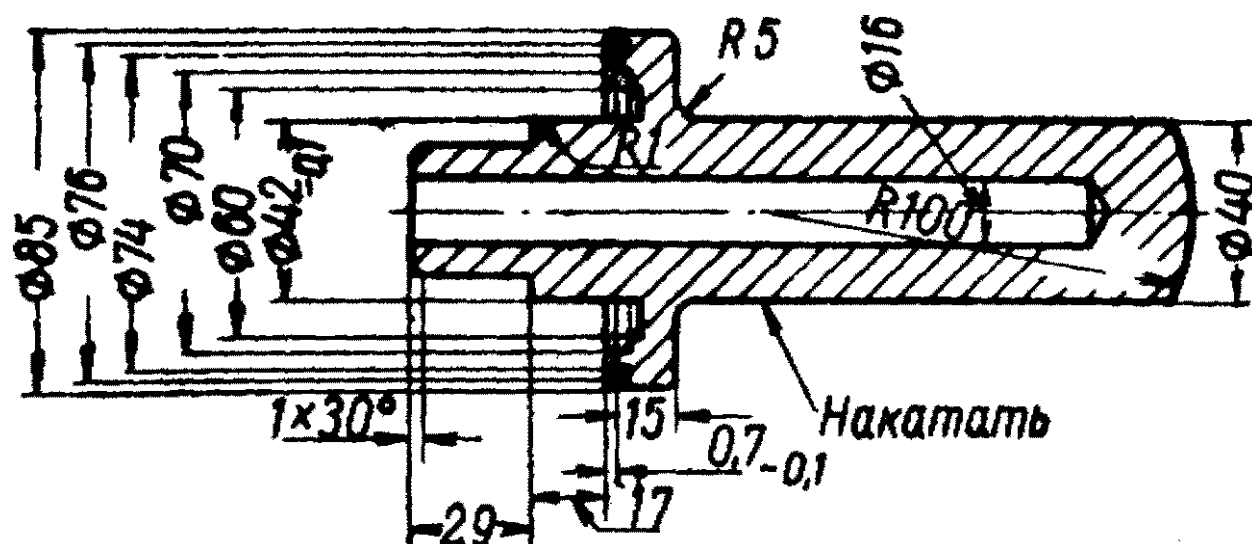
Оправка для запрессовки наружного сальника вала ведущей шестерни
